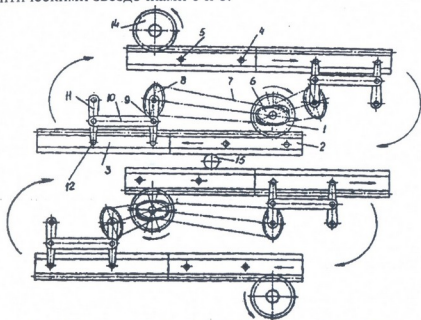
Кинематическая схема станка для поперечной прокатки изделия
